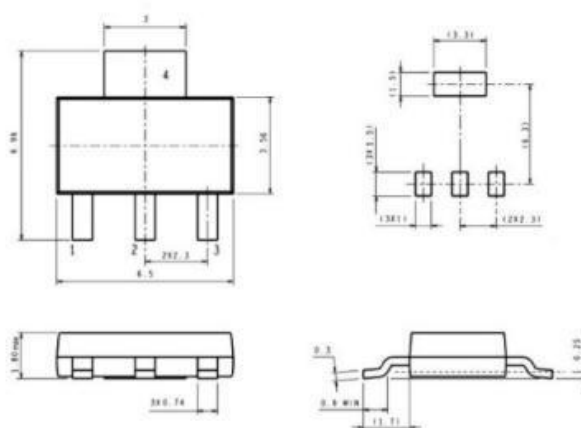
Габаритні розміри стабілізатора L7805
